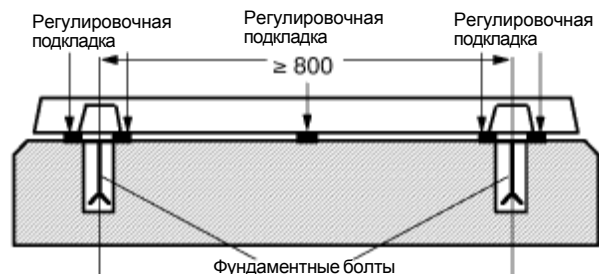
Расположение регулировочных подкладок под опорной плитой
